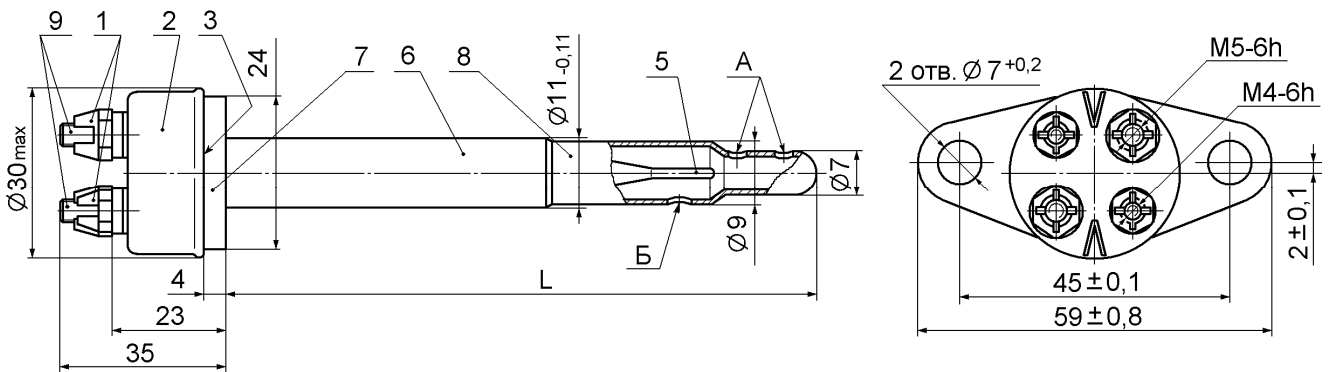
Габаритный чертеж термопреобразователей ТХА-75К, ТХА-100К
